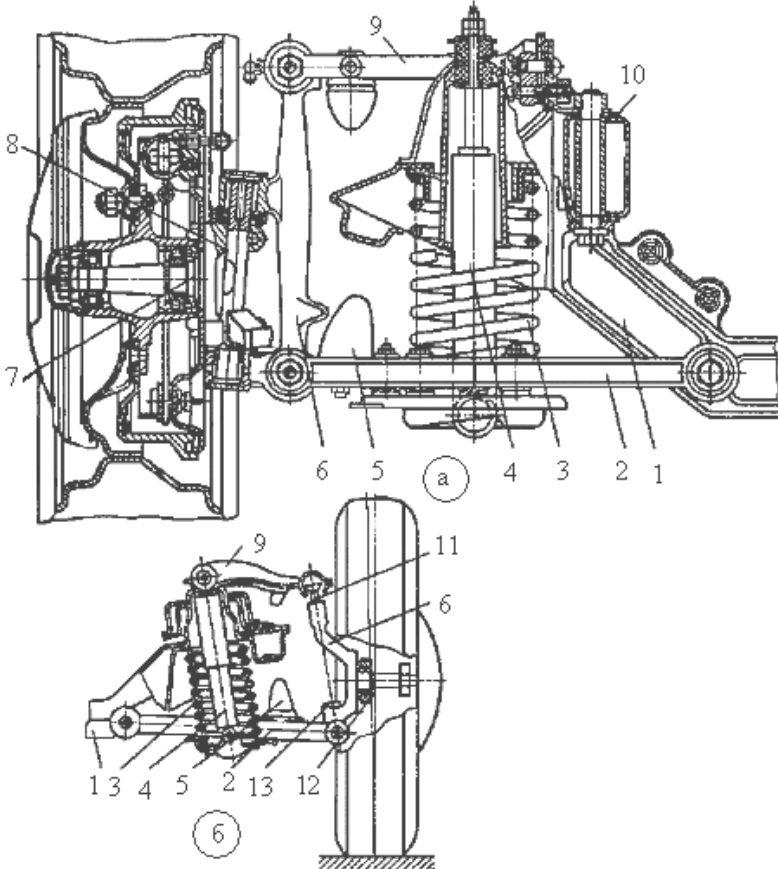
Схема незалежної важільно-пружинної підвіски коліс:
